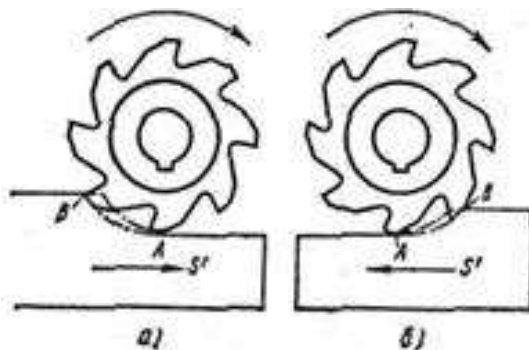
Фрезерование против подачи (а) и по подаче (б) фрезерования называется встречным.
